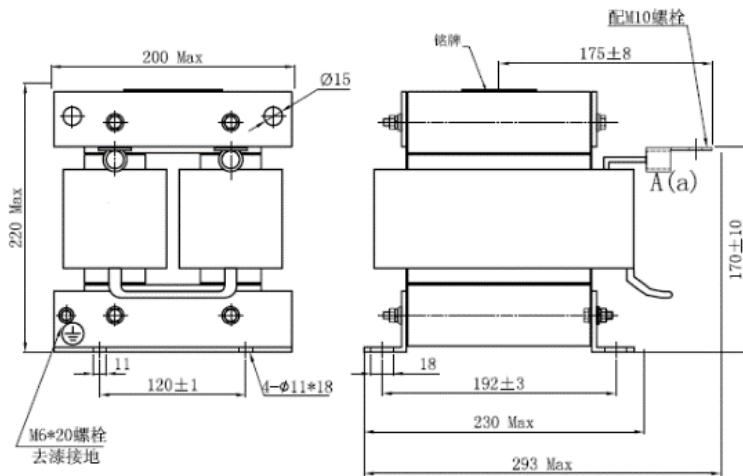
电抗器 DCL150A10006-1 尺寸 (单位: mm)
